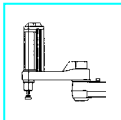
Befestigung des Roboters auf der Montageplatte
